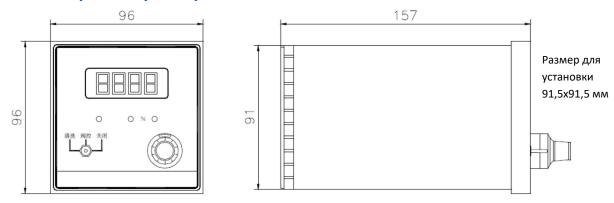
Габаритные размеры корпуса контроллеров D08-1F, 1FP, 1FM
